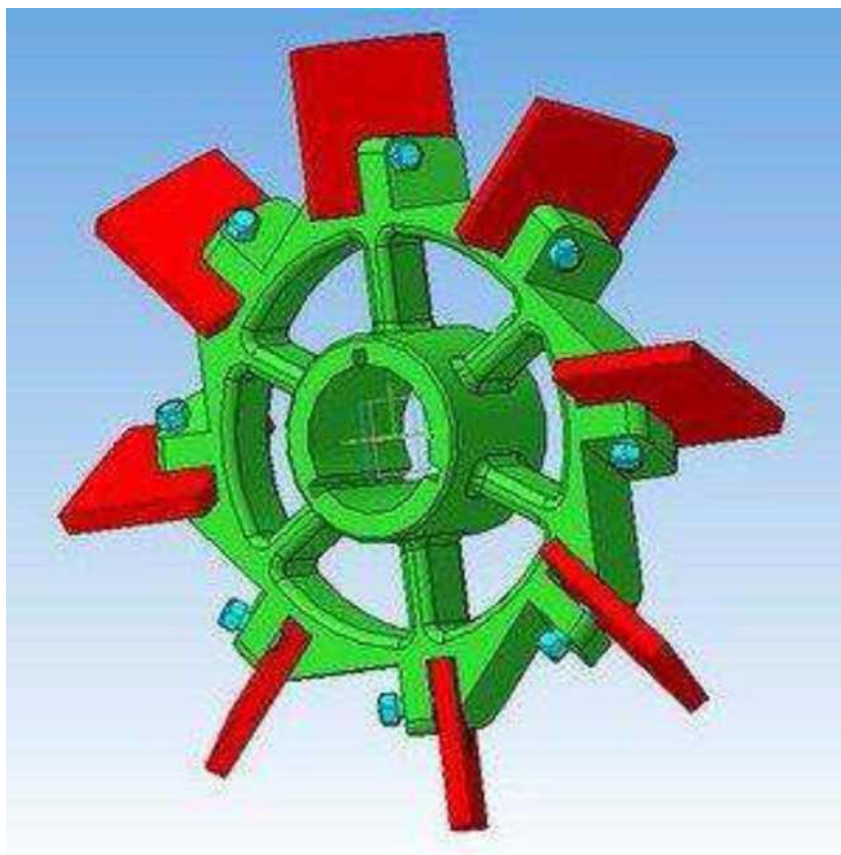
Сборка режущего диска с очищающими ножами
